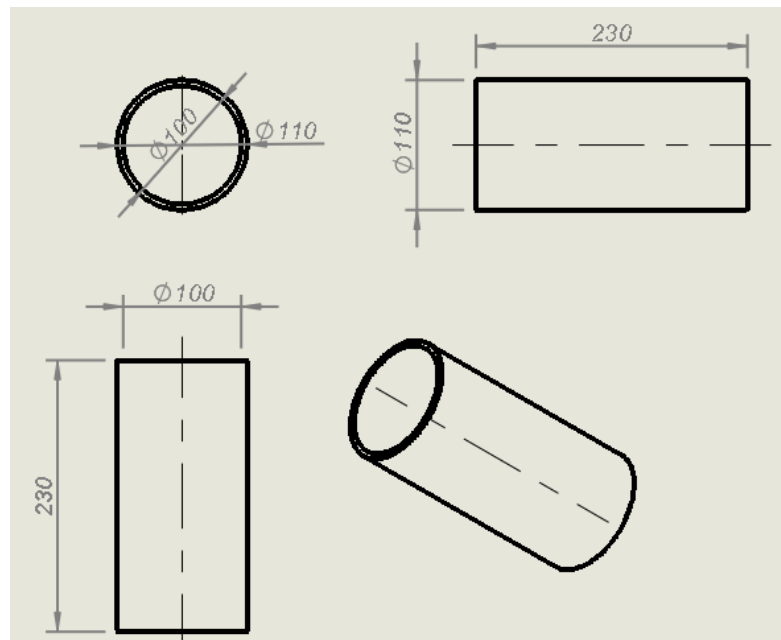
Diseño de cilindro para el bobinado. Medidas en (mm)
